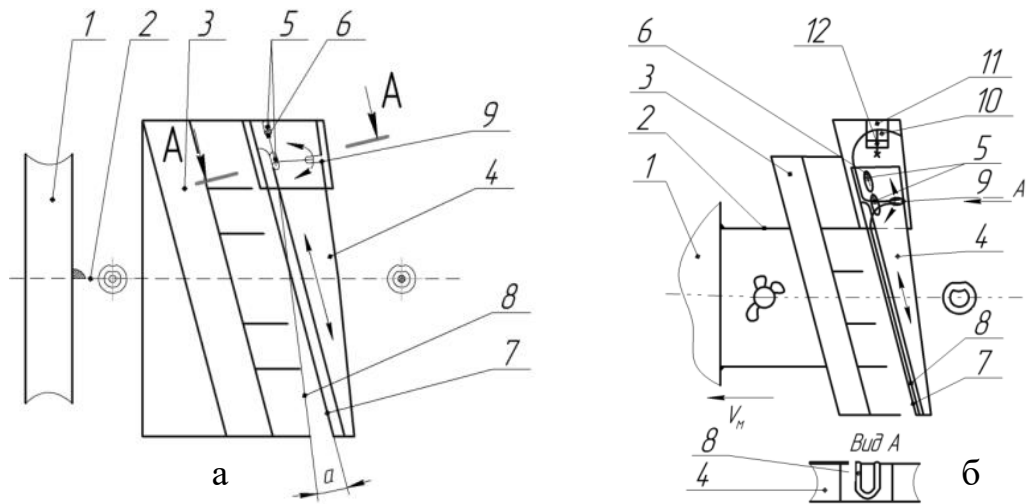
Схема обрізувача гички з головок коренеплодів: 1 – рама обрізувача; 2 – паралелограмний механізм; 3 – гребінчастий копір; 4 – ніж; 5 – нерухома вісь; 6 – поздовжній паз; 7 – кромка ножа; 8 – Г-подібна пружина; 9 – паз ножа; 10 – паз фіксатора; 11 – фіксатор; 12 – гвинт
